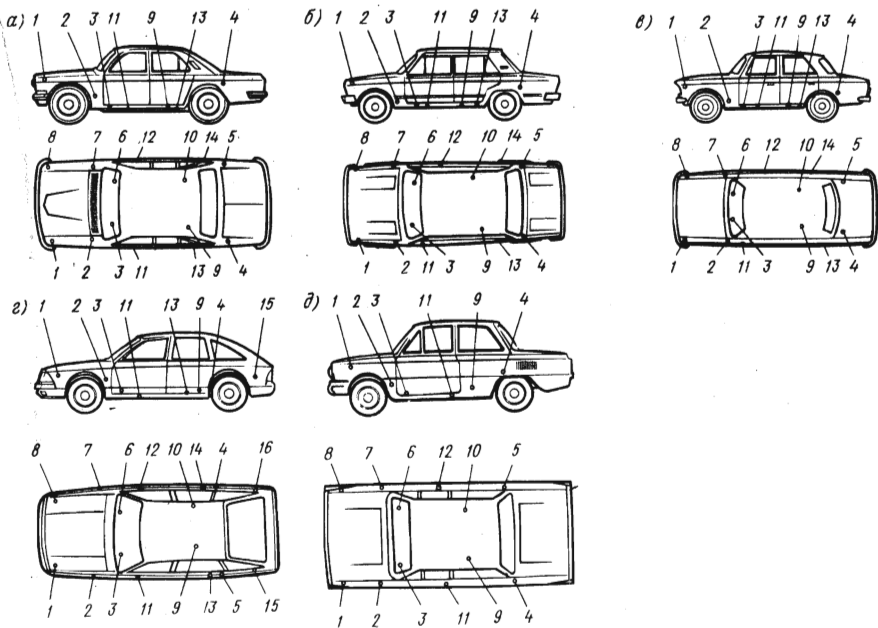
Схема расположения анодов на корпусе автомобилей:
